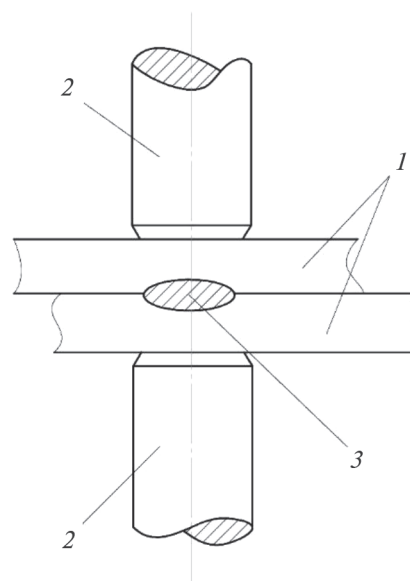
Схема точечной контактной сварки двух деталей: 1 — свариваемые детали; 2 — электроды; 3 — сварочное ядро
